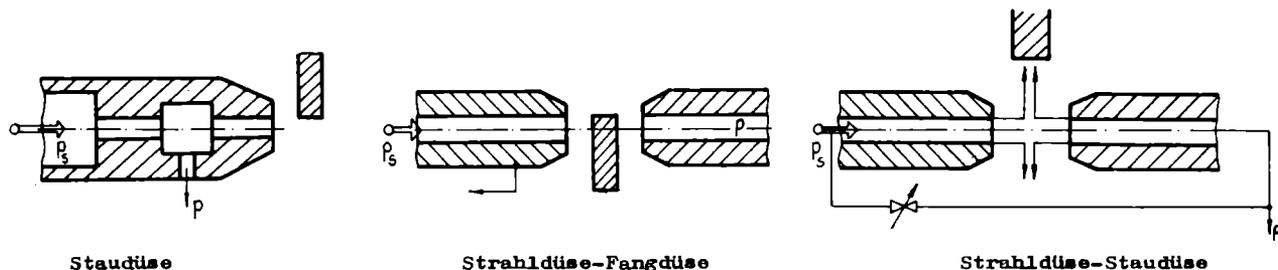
Taktile Sensoren mit pneumatischem Wirkprinzip
